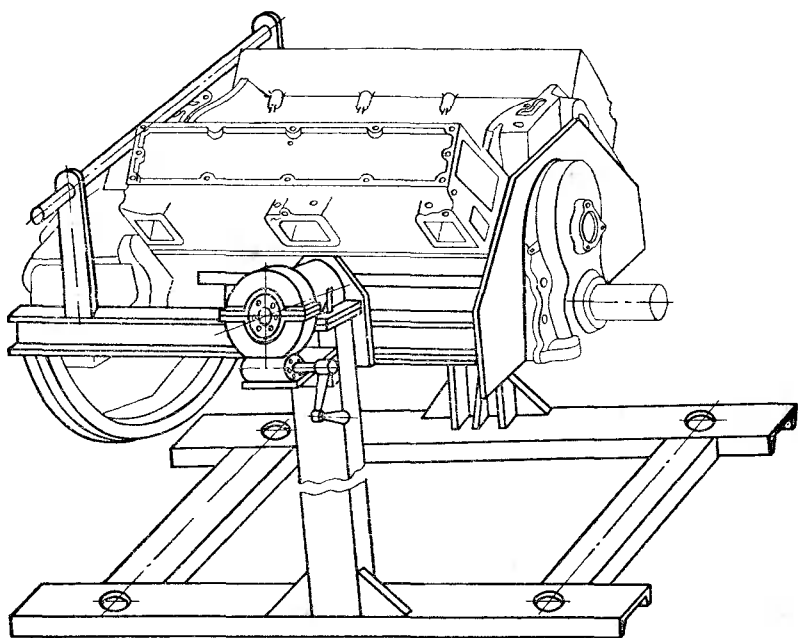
Стенд для разборки двигателей ЗИЛ-130
